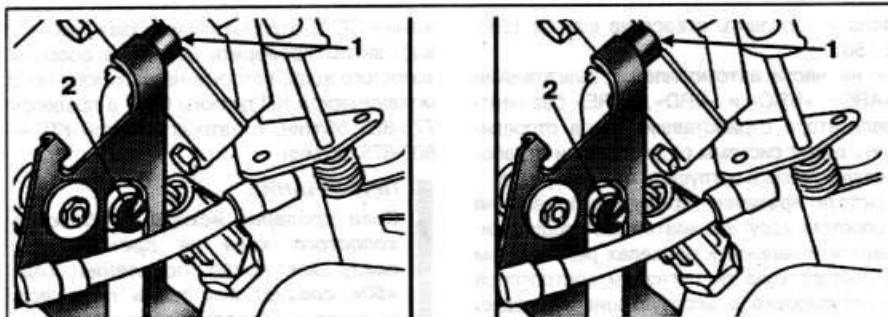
Регулировка исходных оборотов холостого хода (слева двигателя без нейтрализатора, справа двигателя с нейтрализатором):
